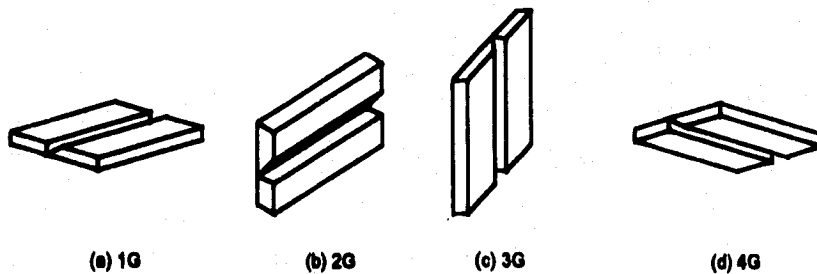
QW-481.3 Posiciones de prueba, para soldaduras de ranura en placa.
